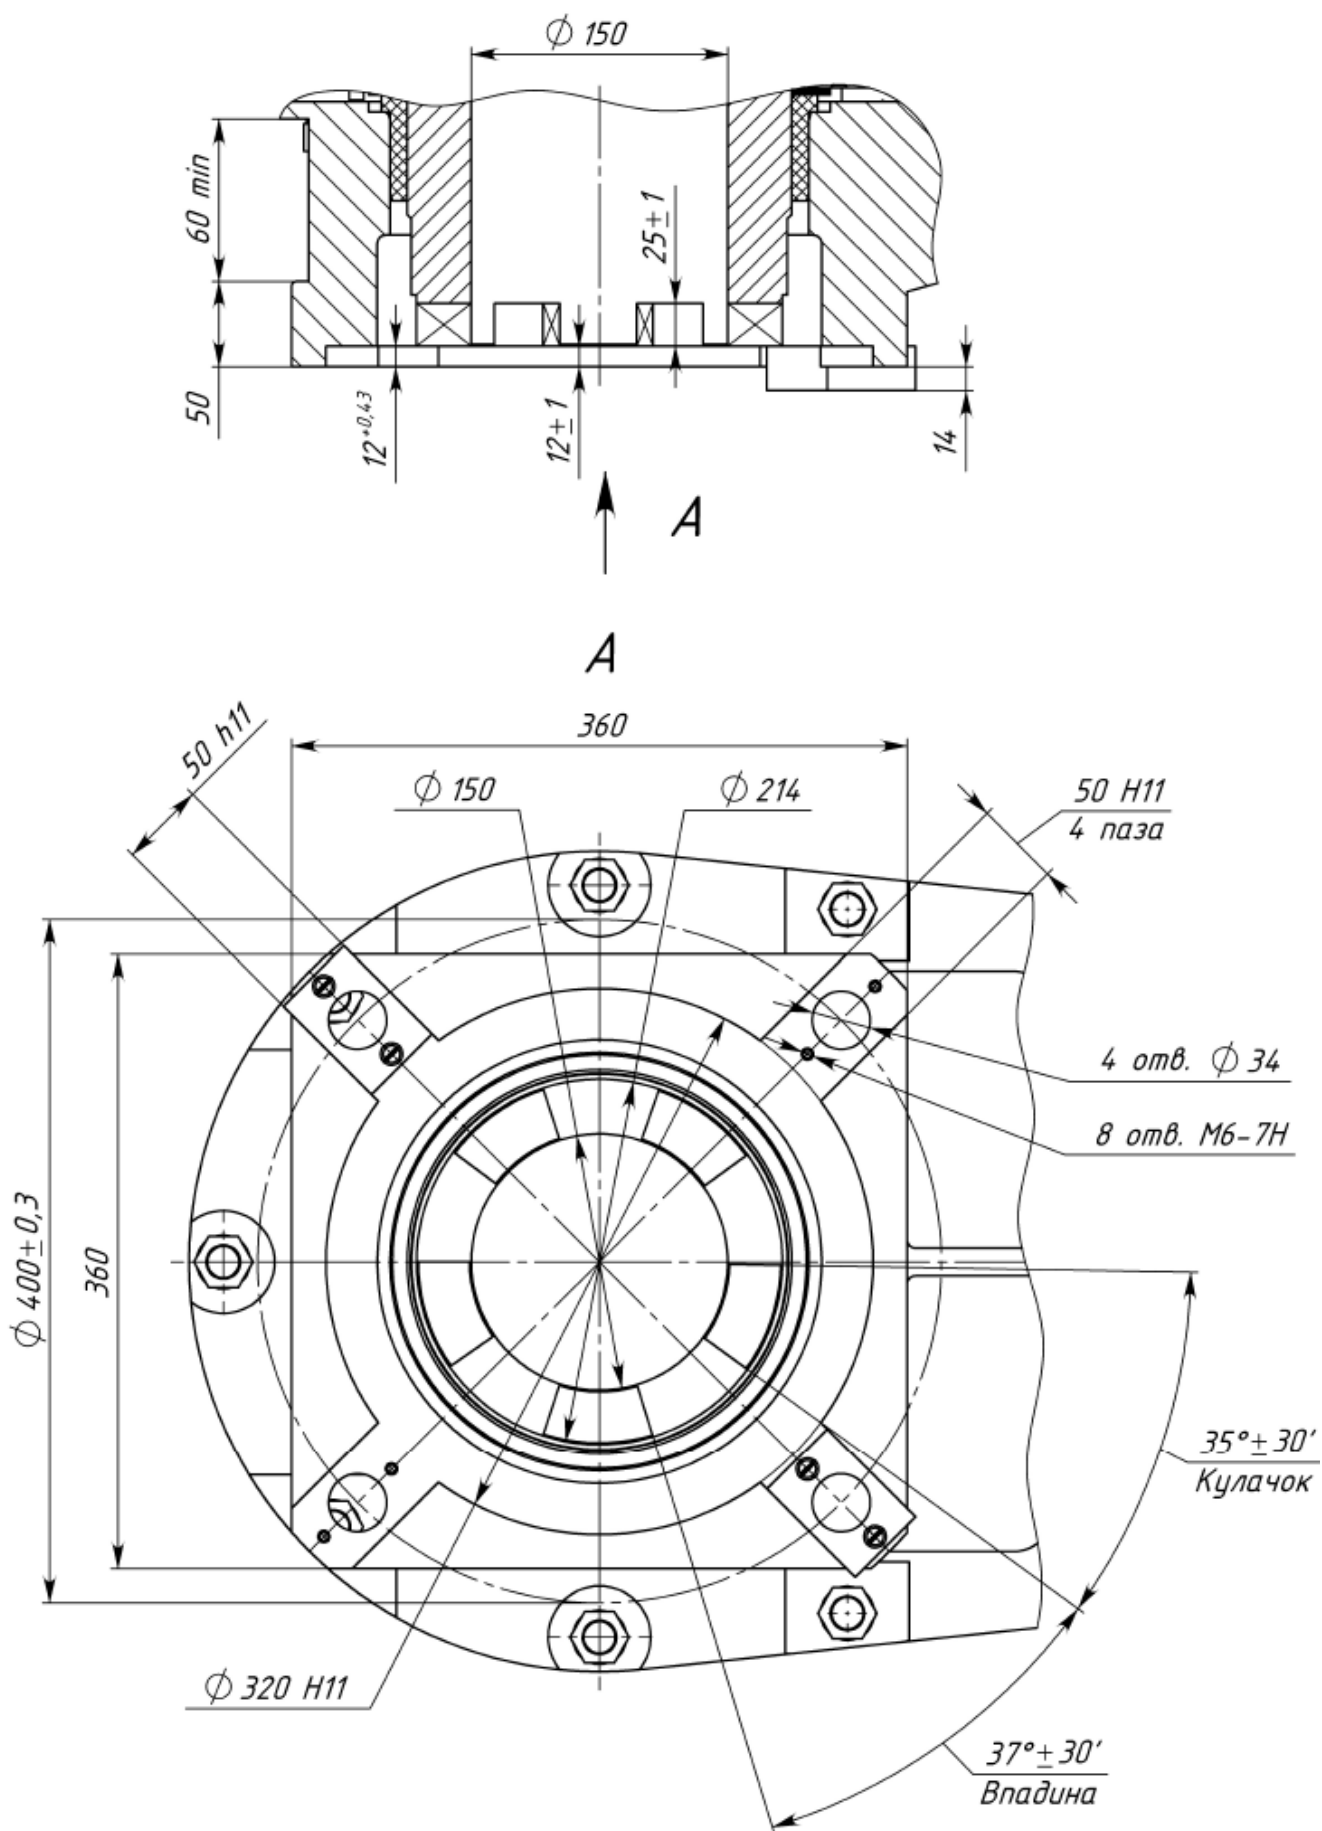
Присоединение типа Д для конструктивной схемы 430
